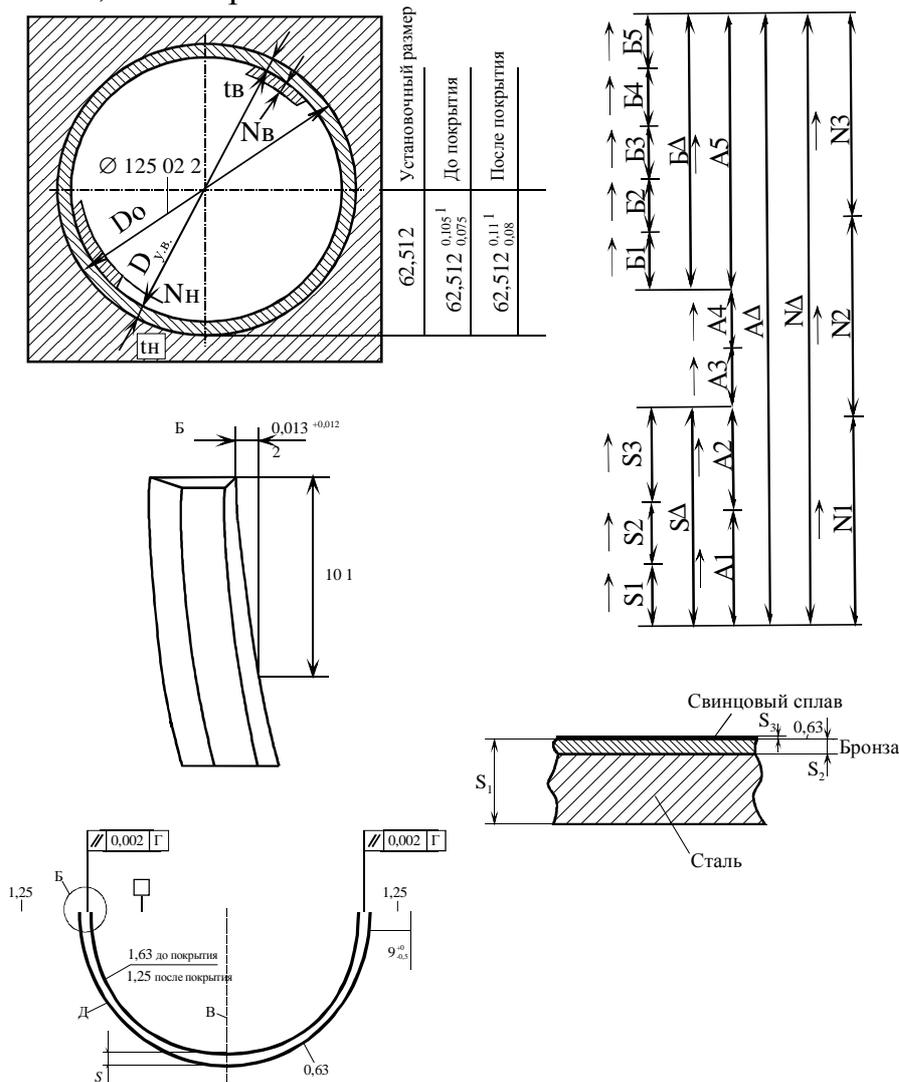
Геометрические параметры вкладышей коренного подшипника и составляющие звенья размерной цепи А условной втулки-подшипника: а – вид сборочного подшипникового узла; б - геометрические параметры «лимонной» расточки; в – вид вкладыша; г- поперечное сечение; д- схема связанных размерных цепей, N_{Δ} – звено - натяг, A_{Δ} - звено - зазор.
